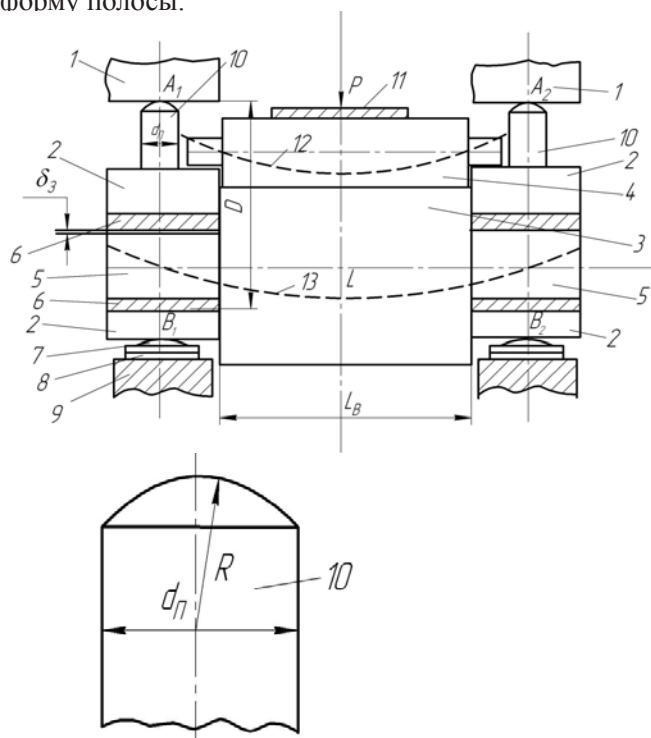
Комплект валков и подушек со сферическими плунжерами: 1 – лапы верхних подушек опорного валка; 2 – лапы подушек нижнего опорного валка; 3 – нижний опорный валок; 4 – нижний рабочий валок; 5 – шейка опорного валка; 6 – подшипник; 7 – прокладка с параболической формой поверхности; 8 – прокладка; 9 – нижняя поперечина станины; 10 – плунжер со сферической формой торца; 11 – полоса; 12 – линия прогиба рабочего валка; 13 – линия прогиба опорного валка (P – сила прокатки; d_n – диаметр плунжера; R – радиус сферической поверхности торца плунжера; $R = 200-500$ мм)
